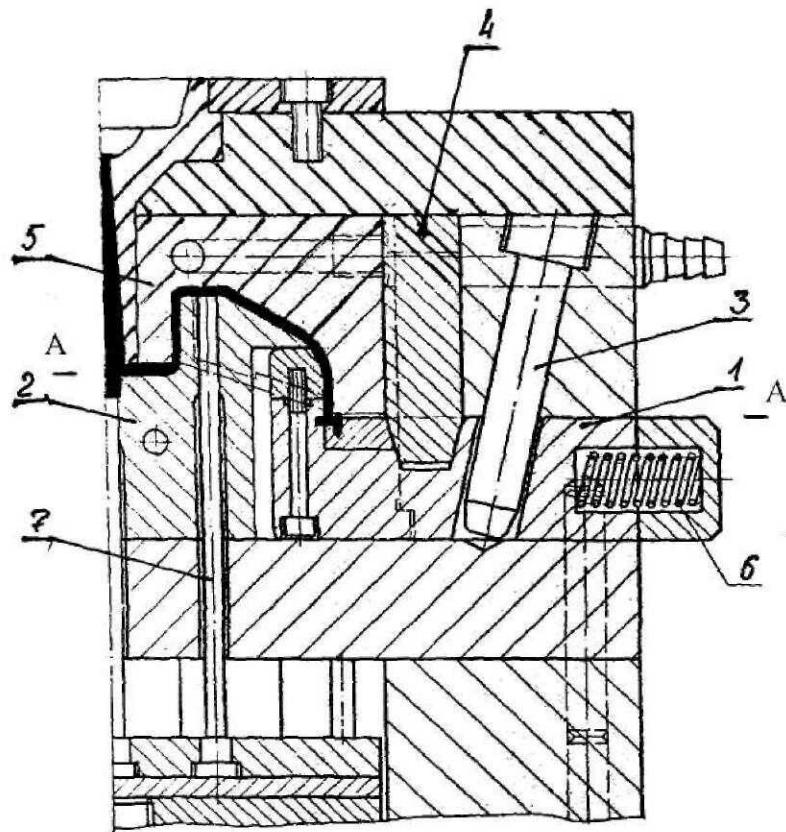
Пресс-форма для изготовления детали «коробка»:
